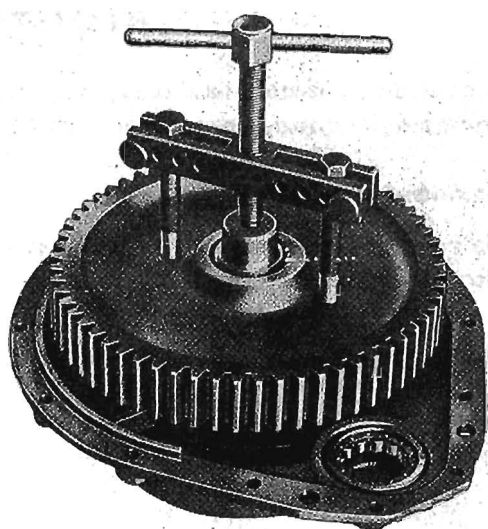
Smontaggio dell'ingranaggio condotto riduttore mediante l'estrattore universale e due viti (16 MB \times 1,5 mm).
